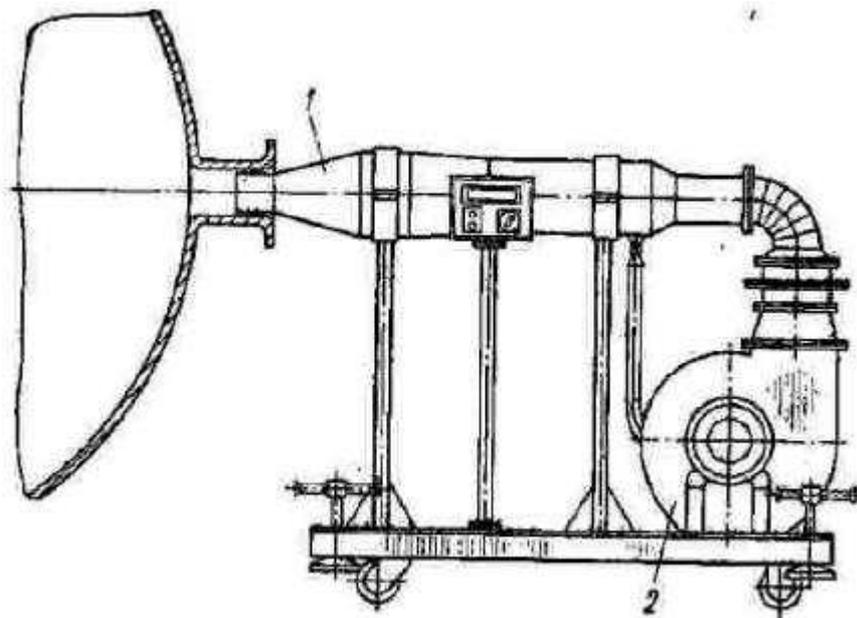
установка для осушки аппарата после гидравлического испытания: 1 – газовый контактный нагреватель; 2 – компрессор.
